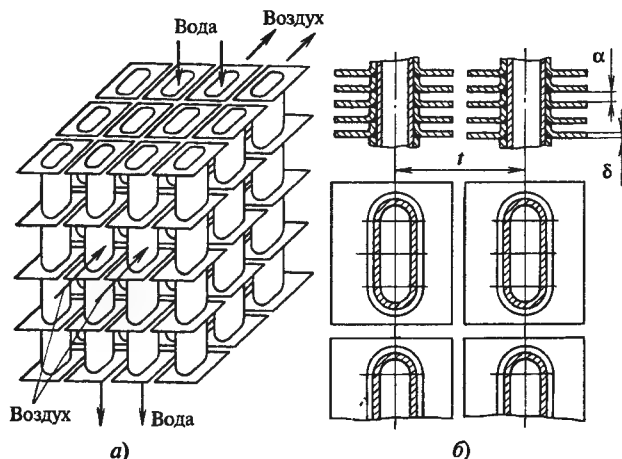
Трубно-пластинчатый воздухоохладитель: а — схема; б — продольный и поперечный разрезы трубок
